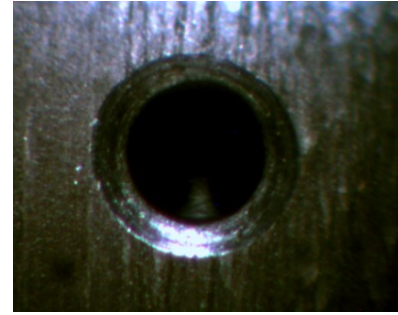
Entgratungsergebnis des Versuchs mit dem Burr-Off-Werkzeug
